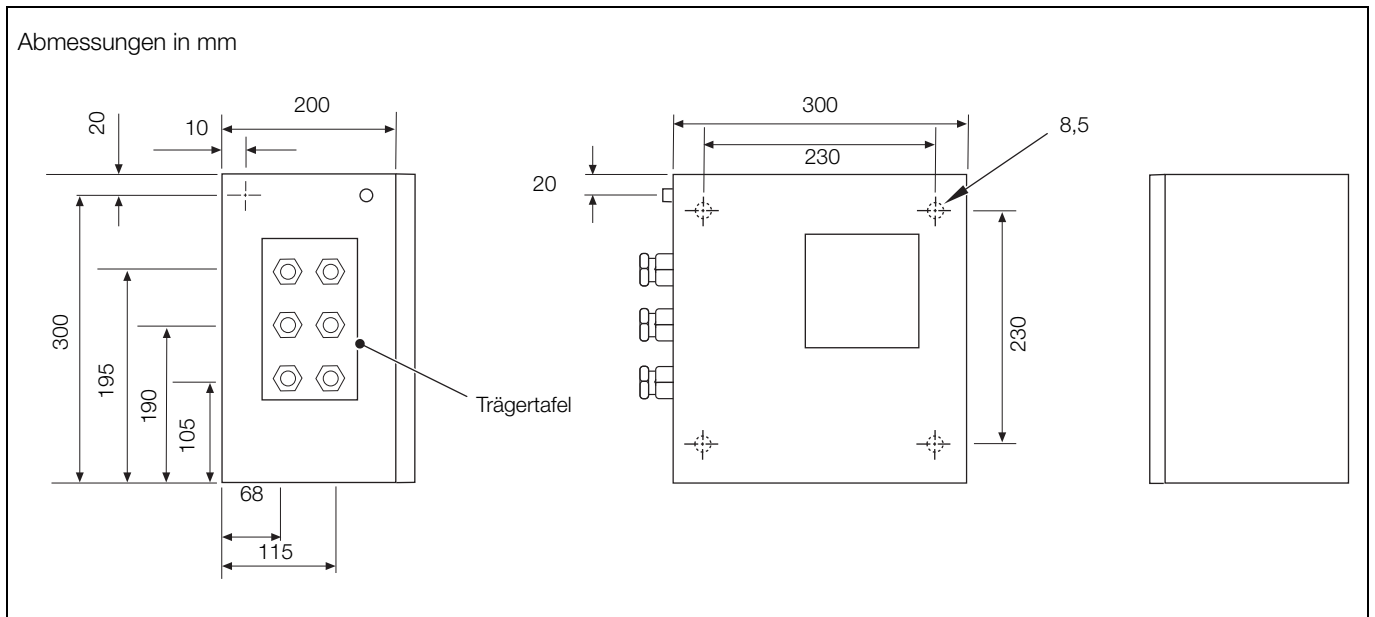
Abmessungen der Messumformereinheit und Details zur Installation
